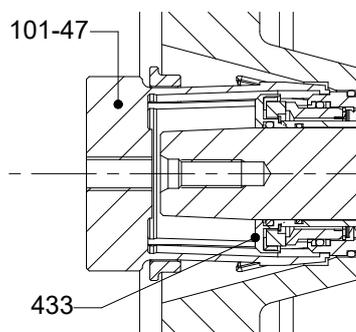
Montaje del cierre mecánico de cartucho doble C022/025M1-4STQ
